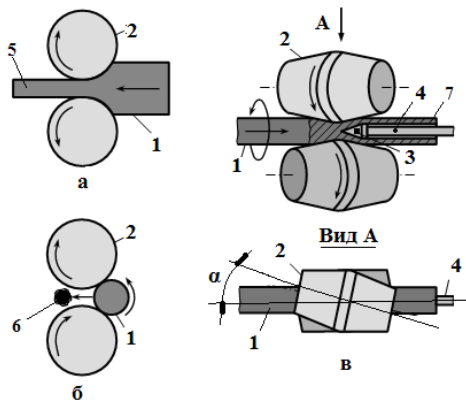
Основні види прокатки: а – поздовжня прокатка; б – поперечна прокатка; в – поперечно-гвинтова прокатка: 1 – заготовка; 2 – валок; 3 – оправка; 4 – стрижень; 5 – продукція прокату (сортовий прокат, стрічки, смуги, листи); 6 – продукція прокату (кулі, осі, шестерні на прокатних станах із зубчастими валками); 7 – продукція прокату (труби, періодичний прокат)
